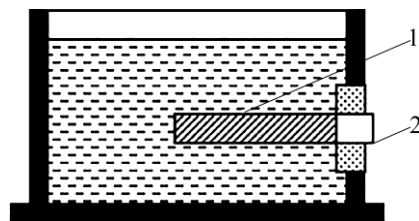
Полный нагрев детали: 1 – обрабатываемая деталь; 2 – токоподвод.
